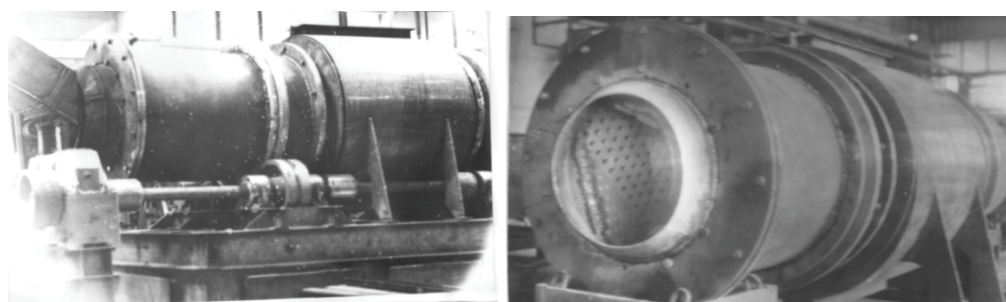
Установка для непрерывной УОЗО обработки деталей и наружный барабан с вмонтированным в нем винтовым ротором
